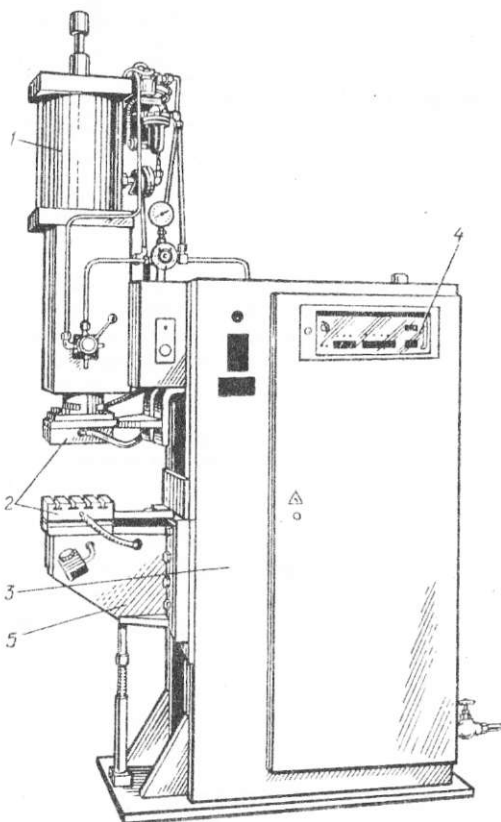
Машина рельсового зварювання типу МР-6916:
